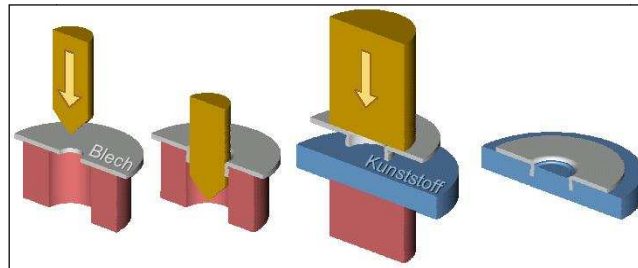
TIPO DE UNIÓN PARA POST-MOLD ASSEMBLY
